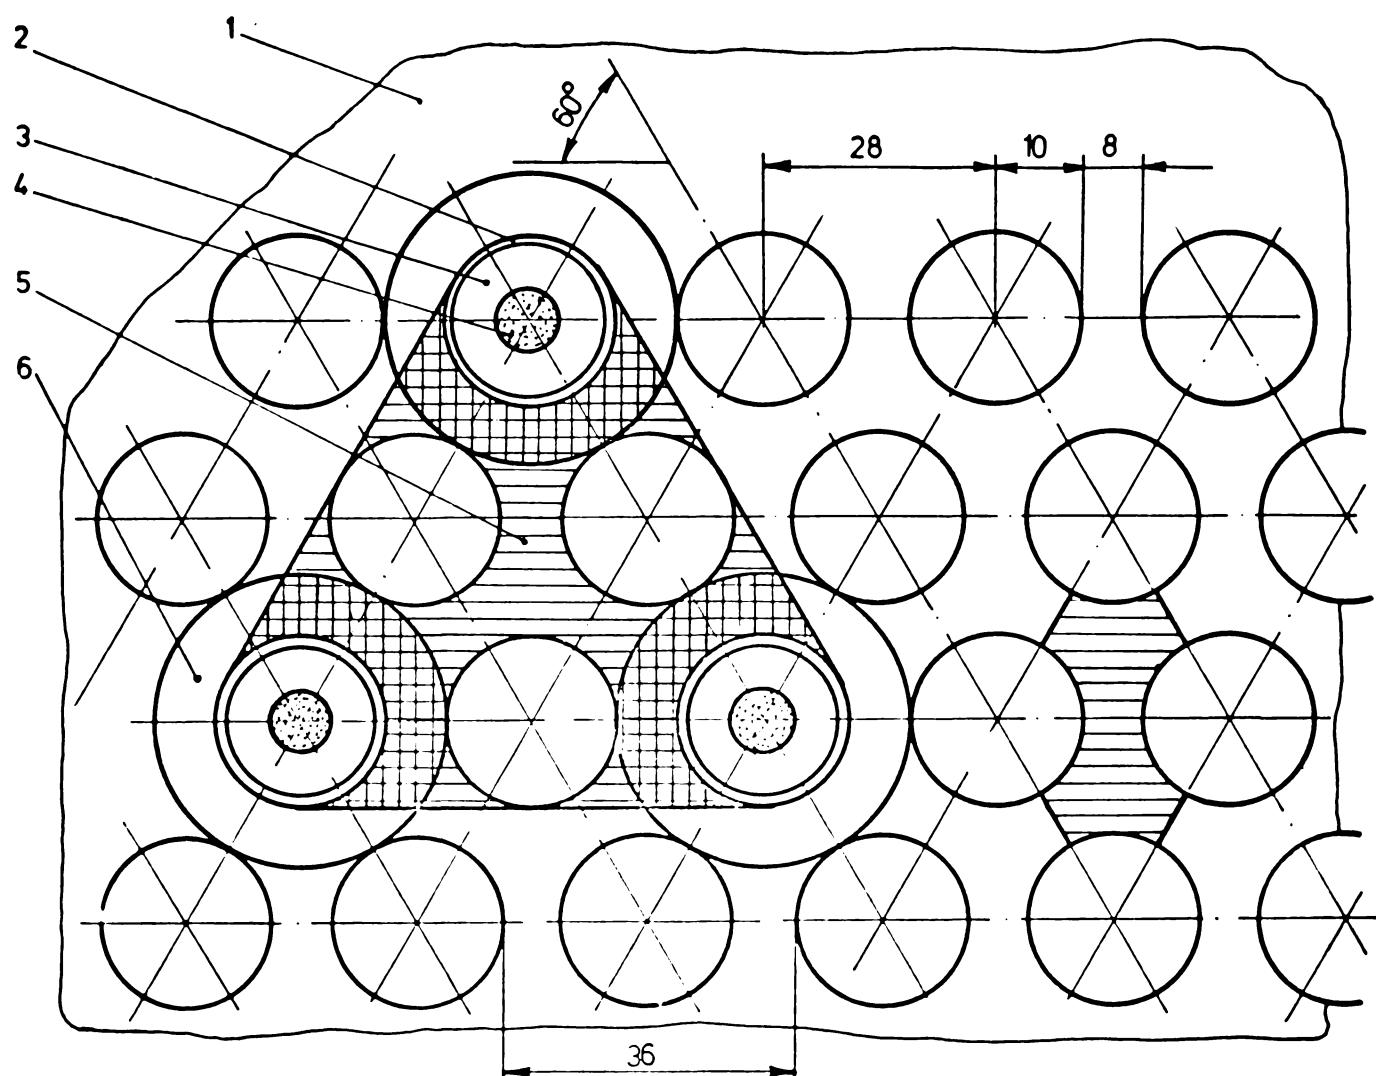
Poziționarea țevilor în placă tubulară și zonele posibile de deformare la mandrinare și sudare prin explozie
